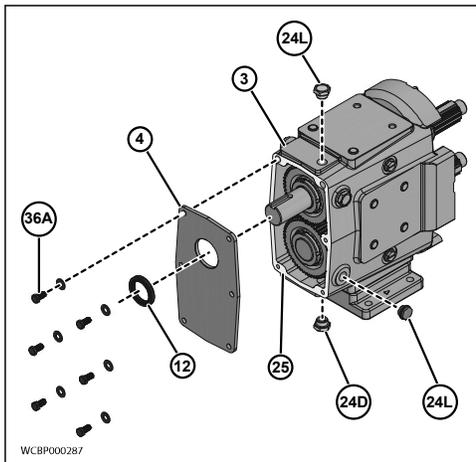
Retirar la cubierta de la caja de engranajes
